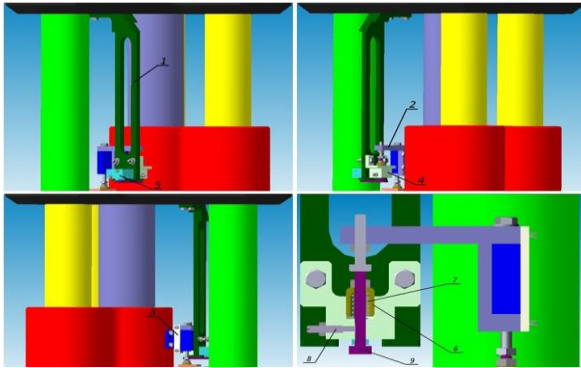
Конструкция блока устройства контроля нижнего положения БГР: 1 – рамка крепежная; 2 – вилка; 3 – пластина (фиксирует вилку на кронштейне); 4 – функциональный блок; 5 – микровыключатель; 6- упор; 7 – пружина; 8 – фиксатор; 9 – толкатель
